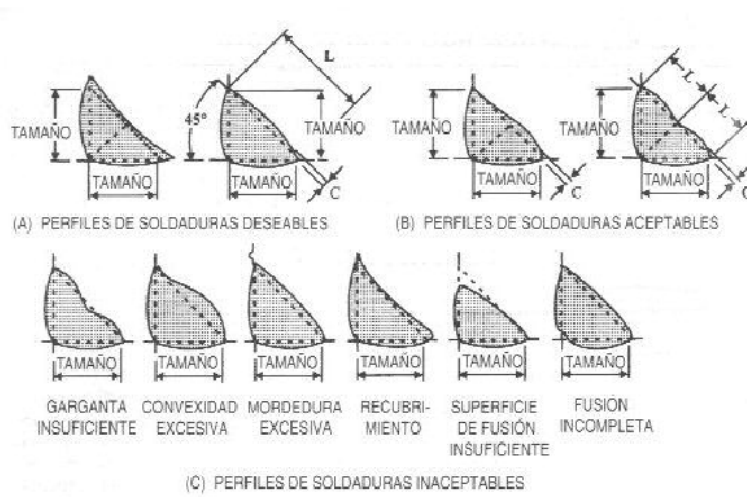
Perfiles de soldadura aceptables e inaceptables para soldaduras en ángulo
